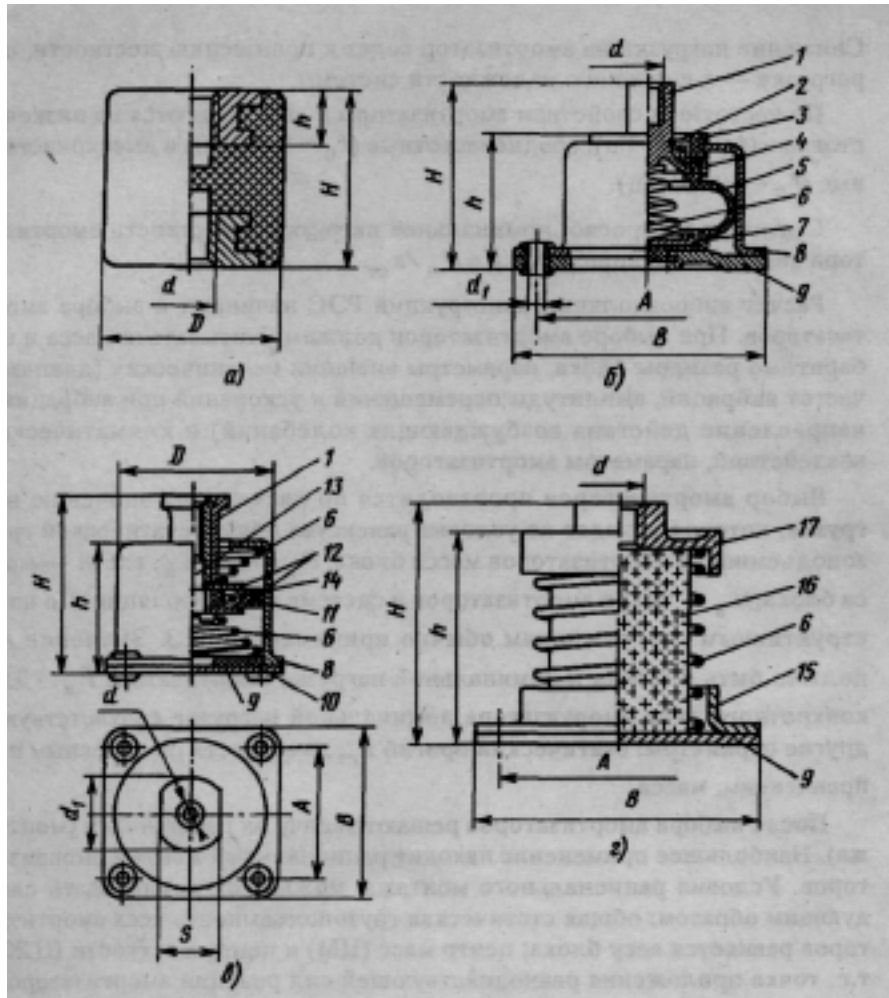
Конструкция амортизаторов: а — «ножка» (АН); б — с воздушным демпфированием (АД); в — пространственного нагружения (АПН); г — пружинно-сетчатый амортизатор; 1 — бобышка; 2 — стопорное кольцо; 3 — резиновое кольцо; 4 — крышка; 5 — баллон; 6 — пружина; 7 — прокладка; 8 — корпус; 9 — основание; 10 — ограничитель; 11 — фрикционные сухари; 12 — шайбы; 13 — винт; 14 — распорное кольцо; 15 — направляющая; 16 — сетчатая подушка; 17 — крышка
